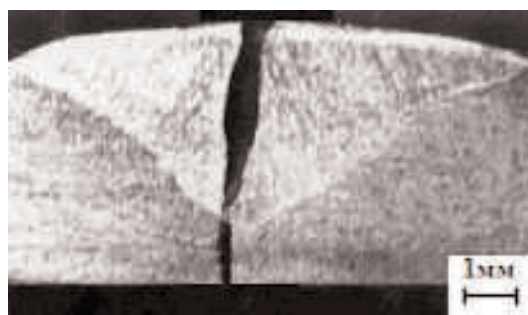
Развитие поры при сварке со смещением дуги со стыка
